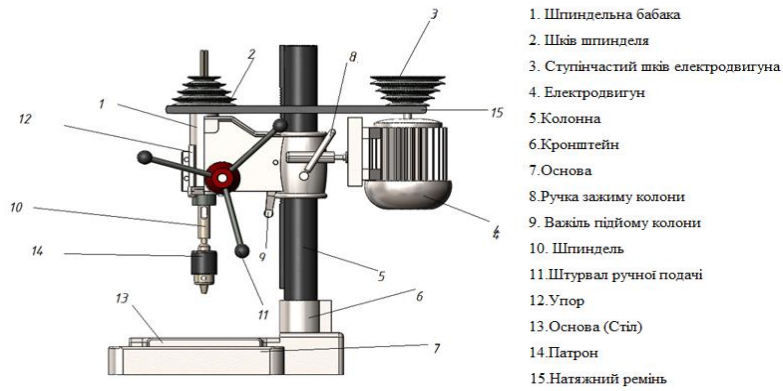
Конструкція механізму свердлильного верстата НС-12А розроблена у програмі SolidWorks
